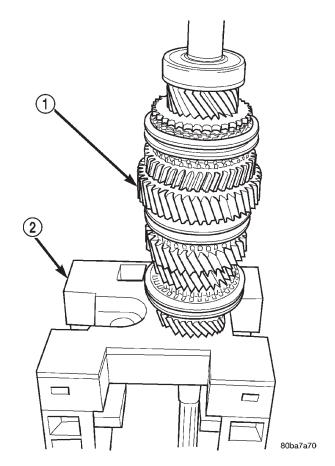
EJE PRINCIPAL SOBRE EL CABALLETE DE APOYO
